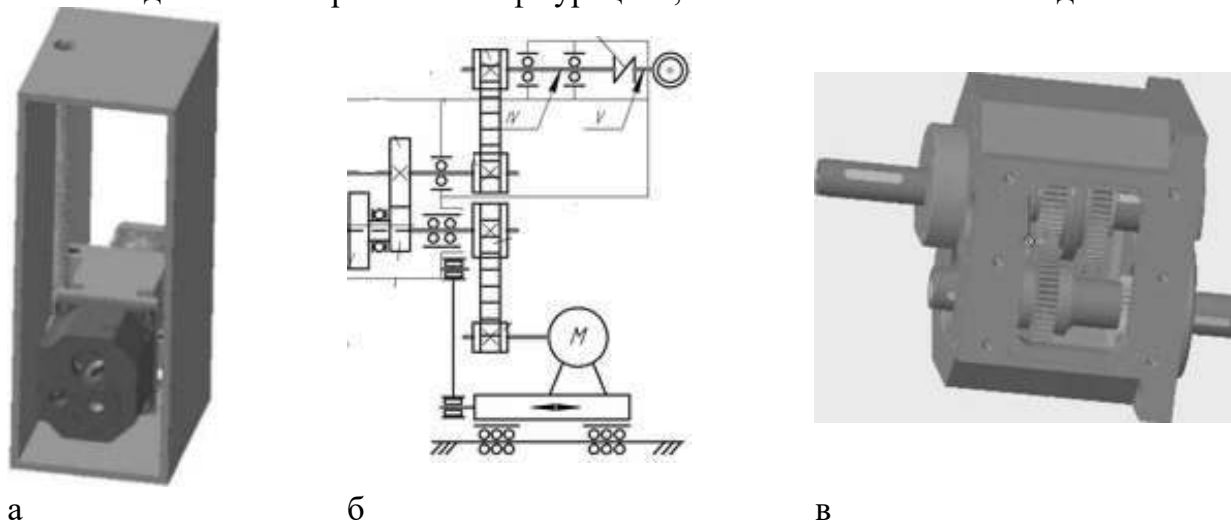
Привод ОЦ: а – компоновка приводу; б – кінематика; в – переріз приводу
